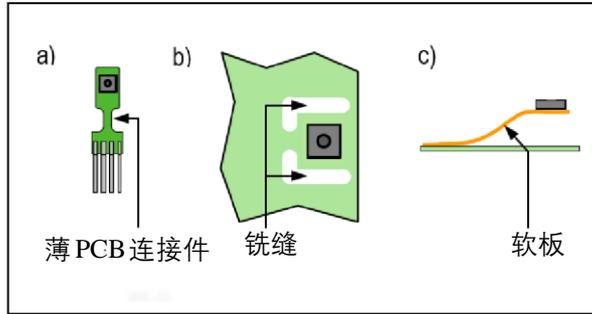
通过小 PCB 板接插或者 PCB 软板连接实现热解耦。
